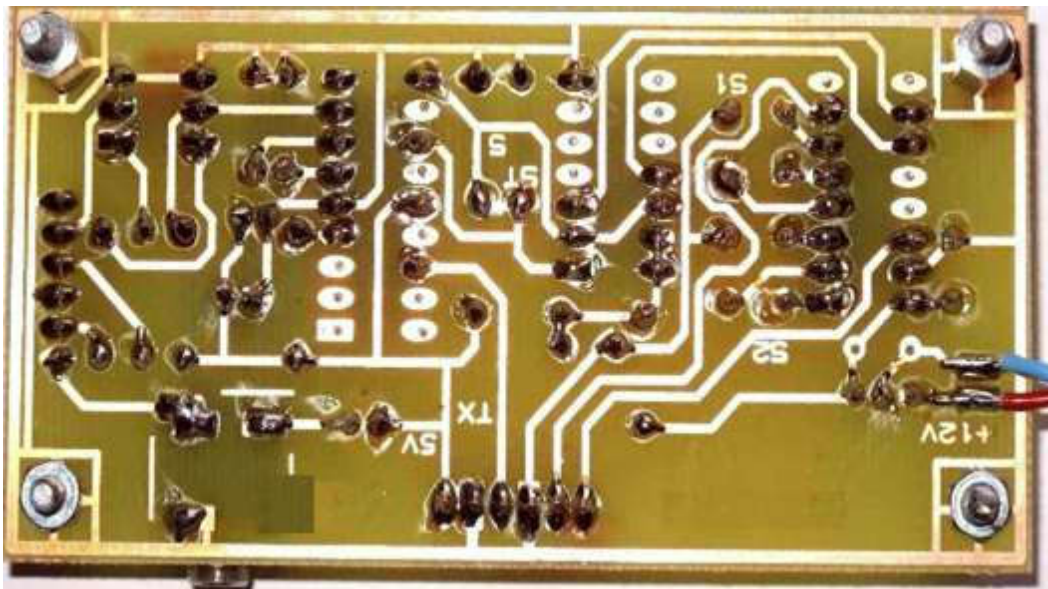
Carte de pilotage vue cote soudures
